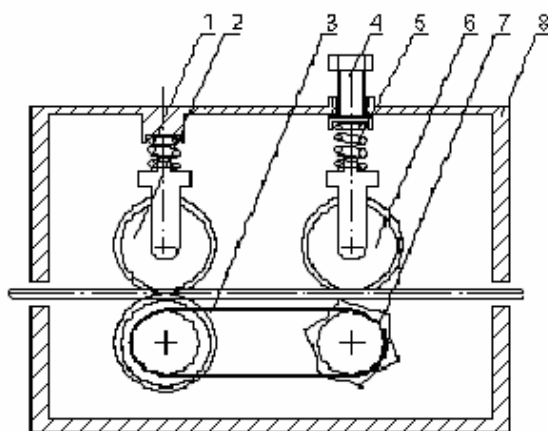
Преобразователь движения: 1) пружина; 2) вспомогательный ролик; 3) задающий ролик; 4) регулирующий винт; 5) регулирующая пружина; 6) регулирующий ролик; 7) управляющий ролик; 8) корпус
